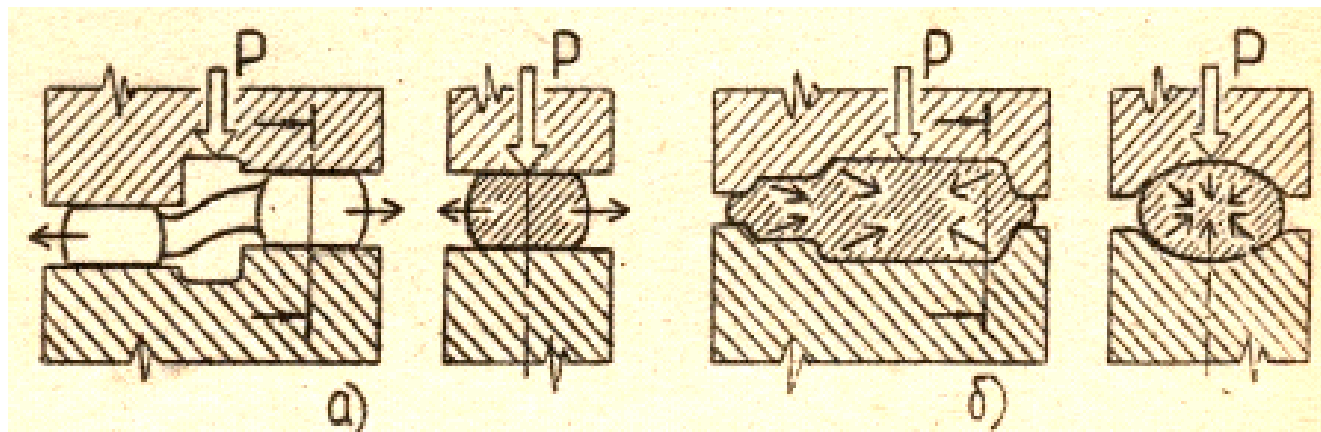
Калибровка поковок (стрелками показаны направления течения металла): а — плоскостная; б — объемная
